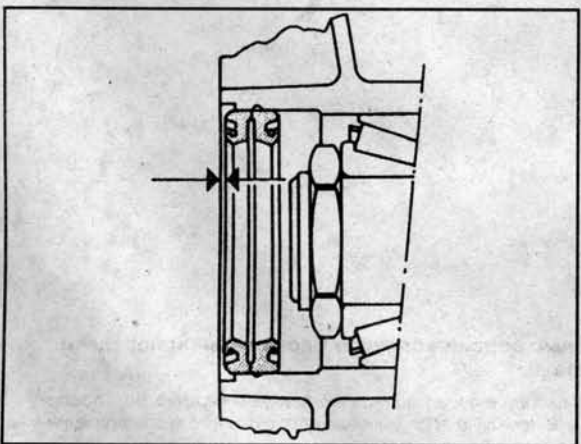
Посадка сальников приводного вала главной передачи
